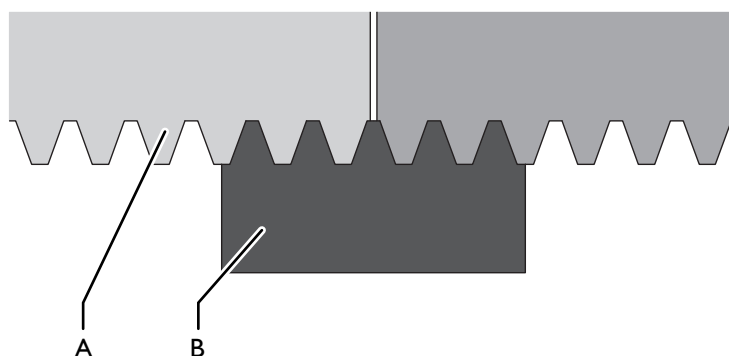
Монтажное приспособление для монтажа зубчатых реек
